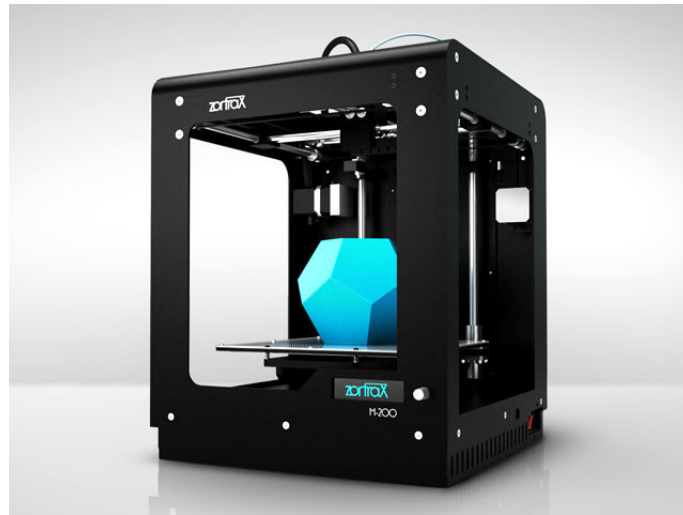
Impresora 3D marca Zortrax M 200 (Fuente: Impresora3dprinter.com)
